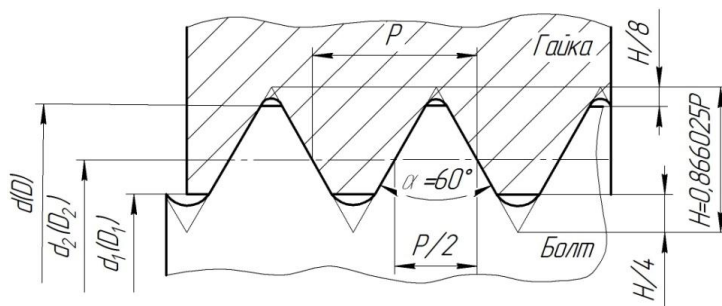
Основные параметры цилиндрических метрических резьб
